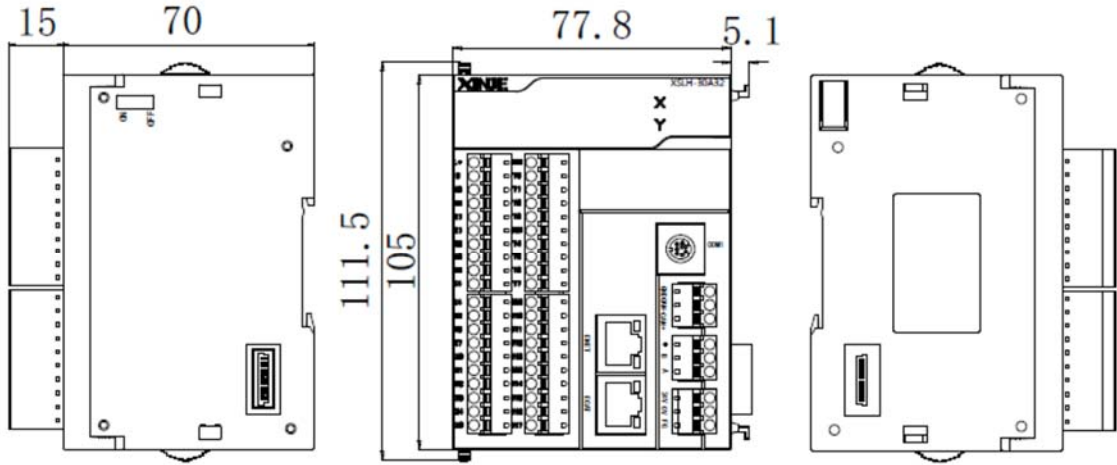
Габаритные и установочные размеры XSLH-30A32
